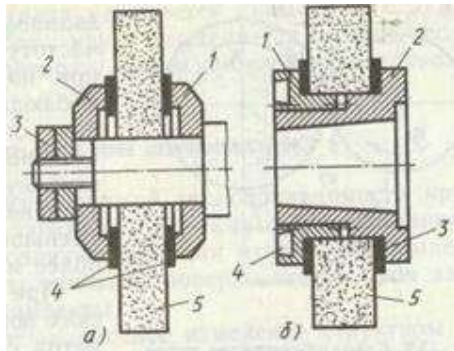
Схеми кріплення шліфувальних кругів: а - фланцями; 1, 2 - фланці, 3 - гайки, 4 - прокладки, 5 - коло; б - на перехідних фланцях; 4 - кільцевий паз, 3 - прокладки
